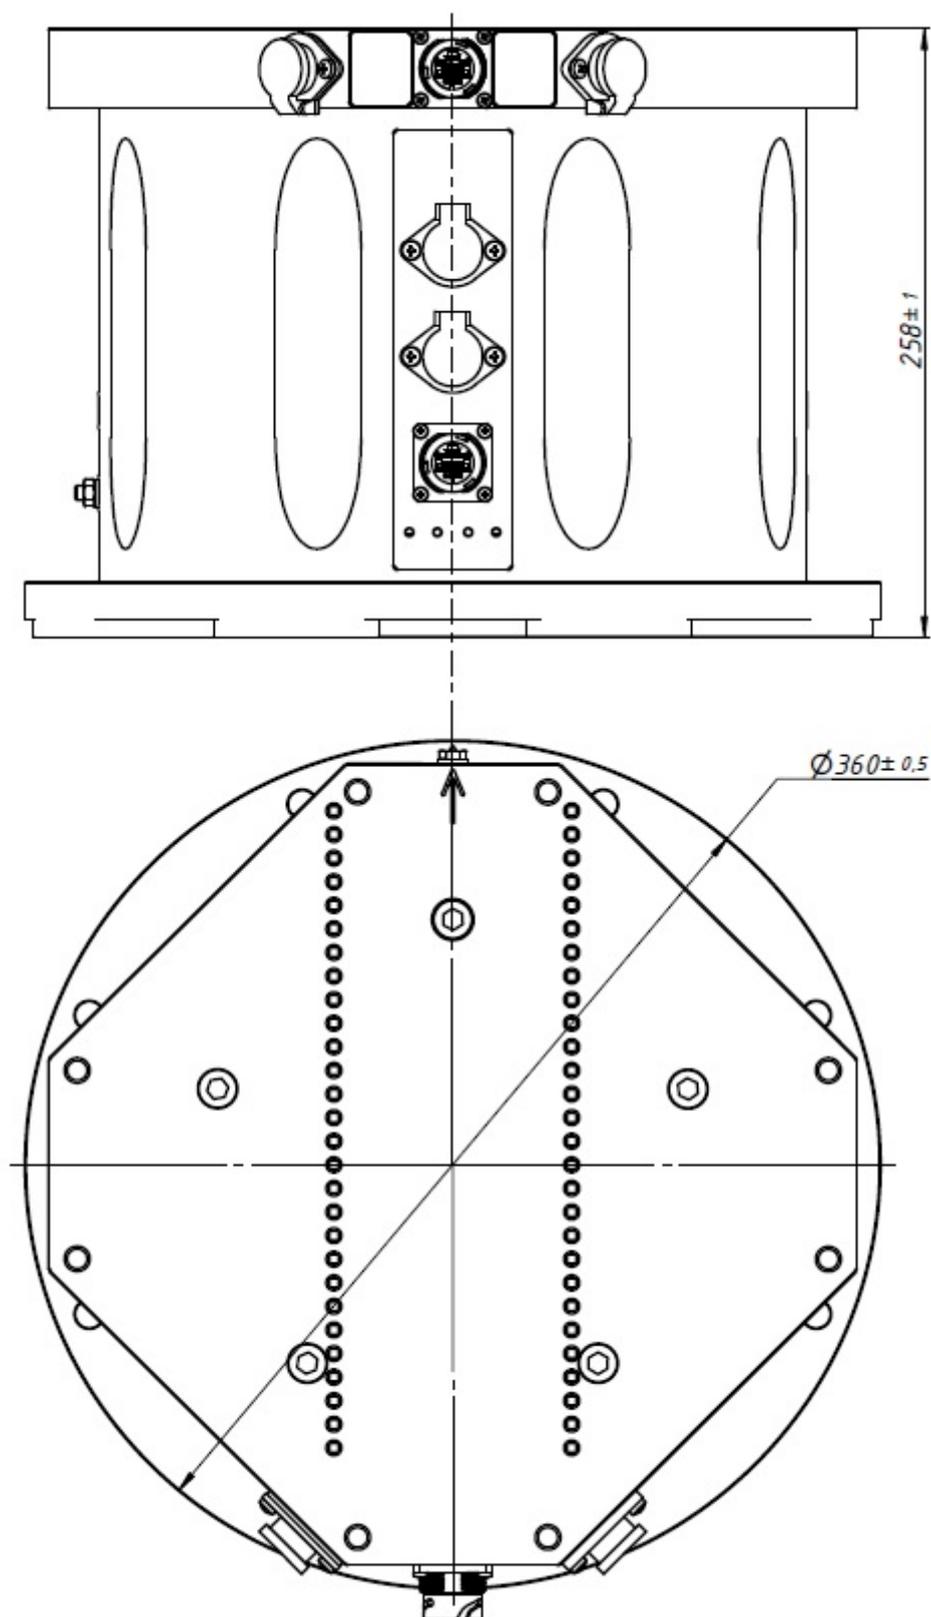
Габаритные размеры опорно-поворотного устройства
